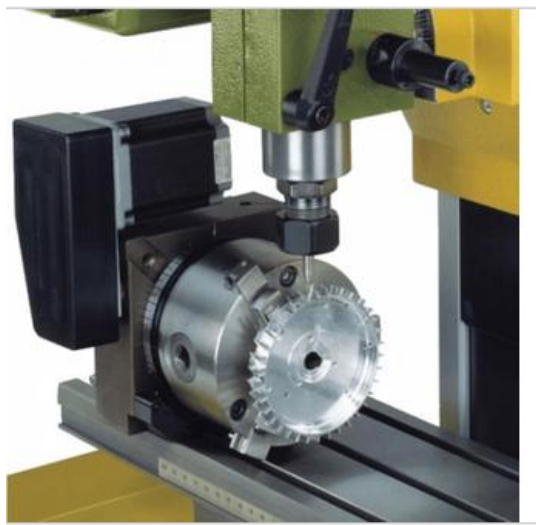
Ділильна головка UT 400/CNC – 24423.
